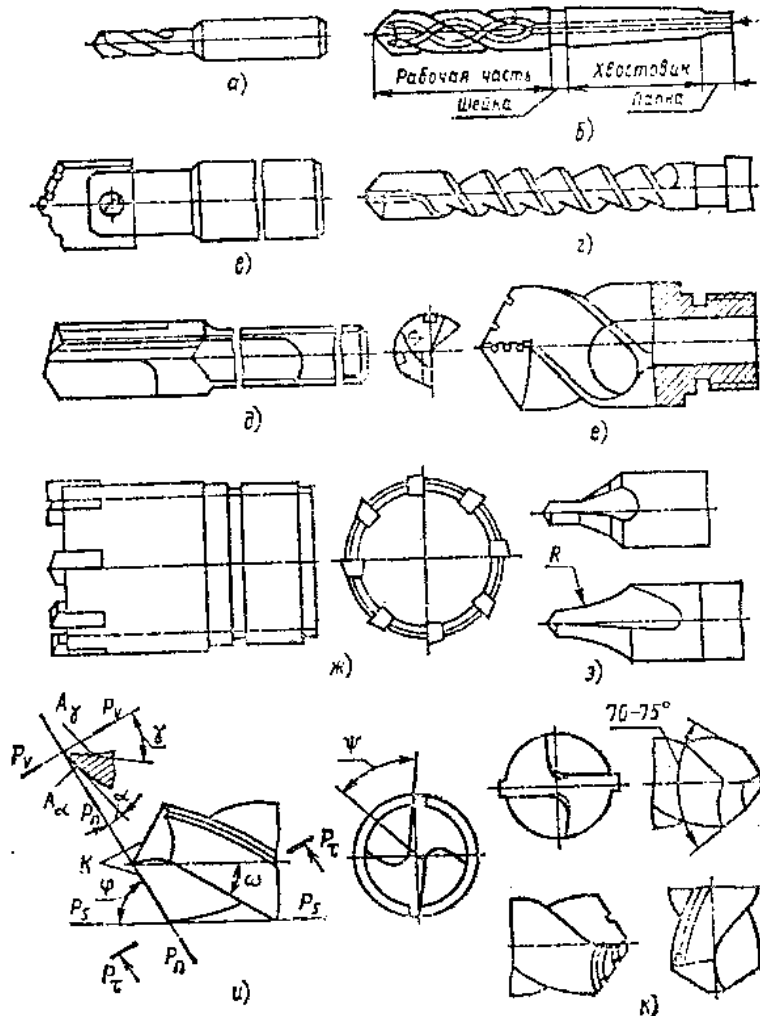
Конструкции сверл (а—з), геометрические параметры режущей части (и) и формы заточки (к)
